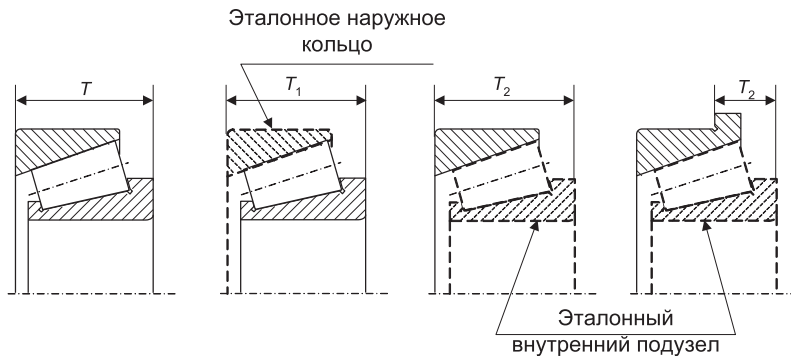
Обозначения основных размеров радиальных и радиально-упорных подшипников
